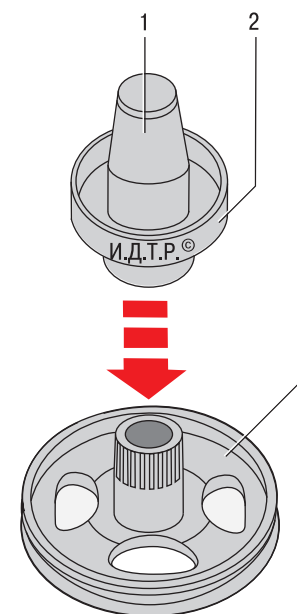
Установка сальника на шкив коленчатого вала двигателя Duratec объемом 1,3 л: 1 – установочная втулка; 2 – сальник; 3 – ступица шкива
